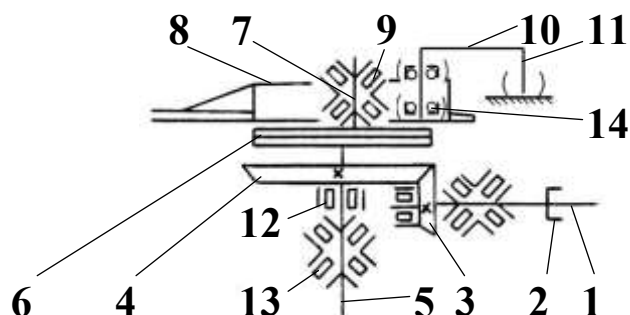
Кинематическая схема редуктора питателя проходческого комбайна
